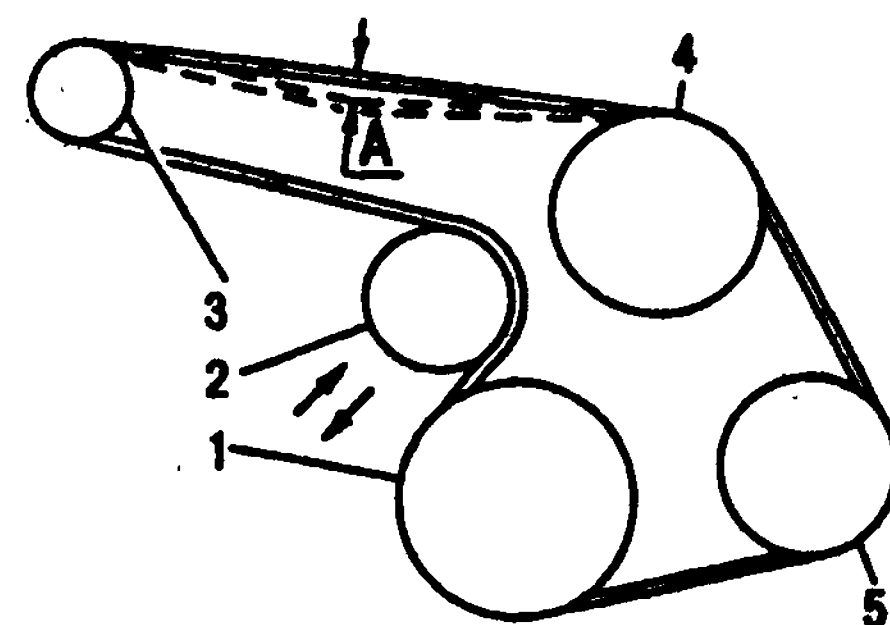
Схема натяжения ремня привода агрегатов: 1 - шкив коленчатого вала; 2 - натяжной ролик; 3 - шкив генератора; 4 - шкив водяного насоса; 5 - шкив насоса ГУР
